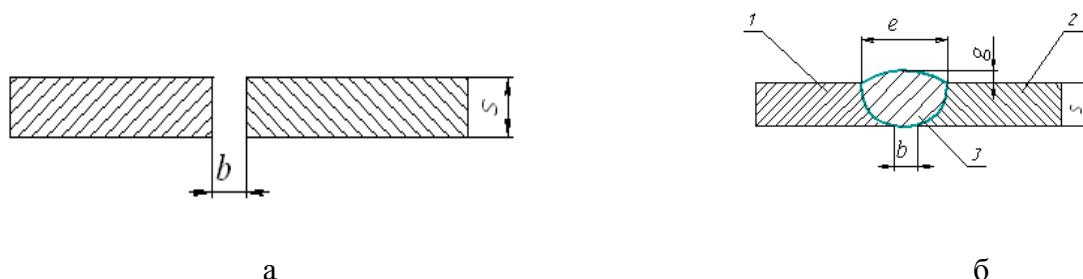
а - форма поперечного сечения подготовленных кромок деталей для сварного соединения С2 до сварки, б – форма поперечного сечения сварного соединения С2 после сварки:  $s$  – толщина детали,  $b$  – расстояние между кромками деталей до сварки  $s = 3$  мм,  $b = 1,0-2,0$  мм,  $e = 6$  мм,  $g = 2$  мм, 1, 2 свариваемые детали, 3 – сварной шов
